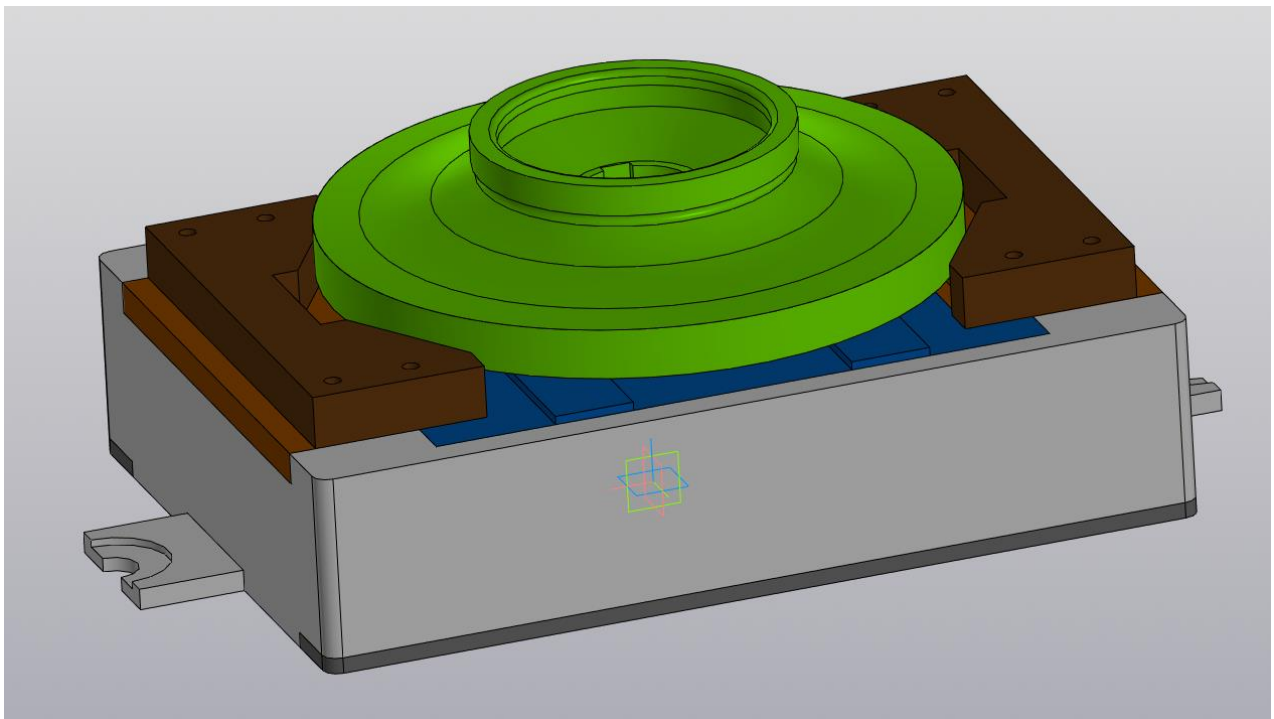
Спроектований верстатний пристрій та закріплена деталь
